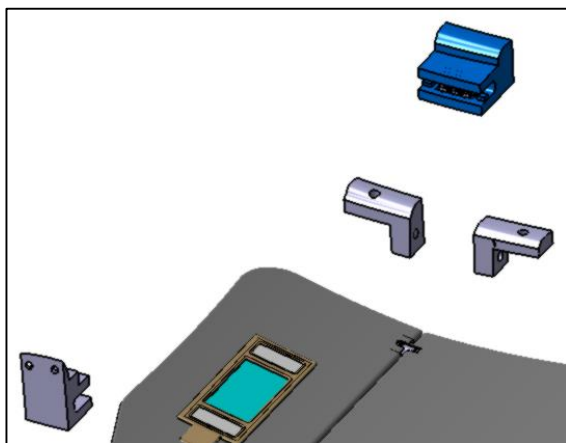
modelação virtual “CATIA V5” em técnica explodida do motor (fonte própria)
